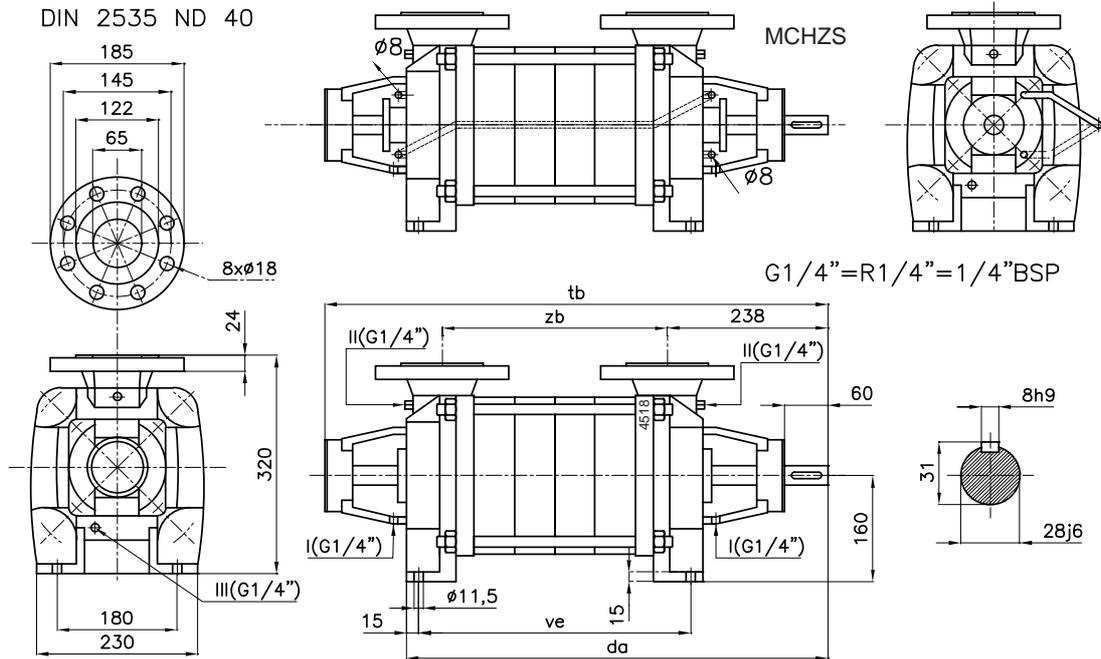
Габаритный чертеж MCHZ(S) 16.
